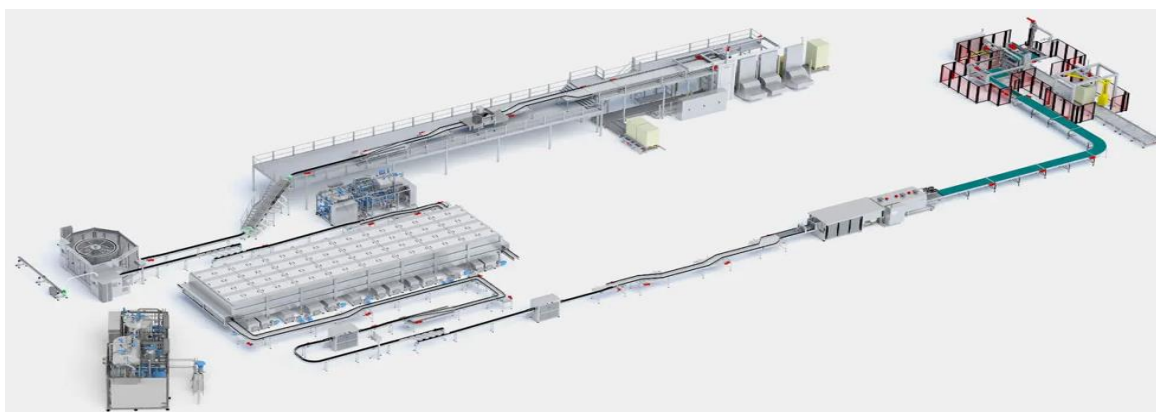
Exemplo de uma linha de montagem (planta/layout fabril).
